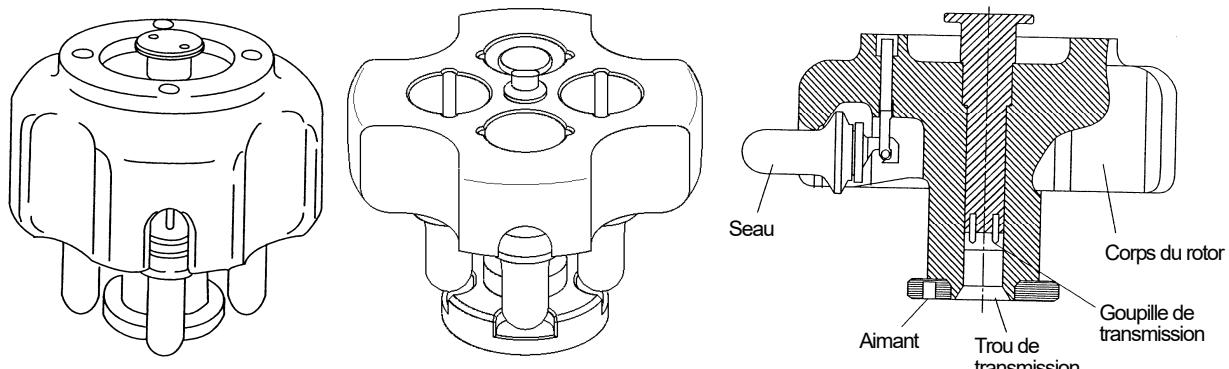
Apparence et noms des pièces du rotor oscillant à réglage rapide
